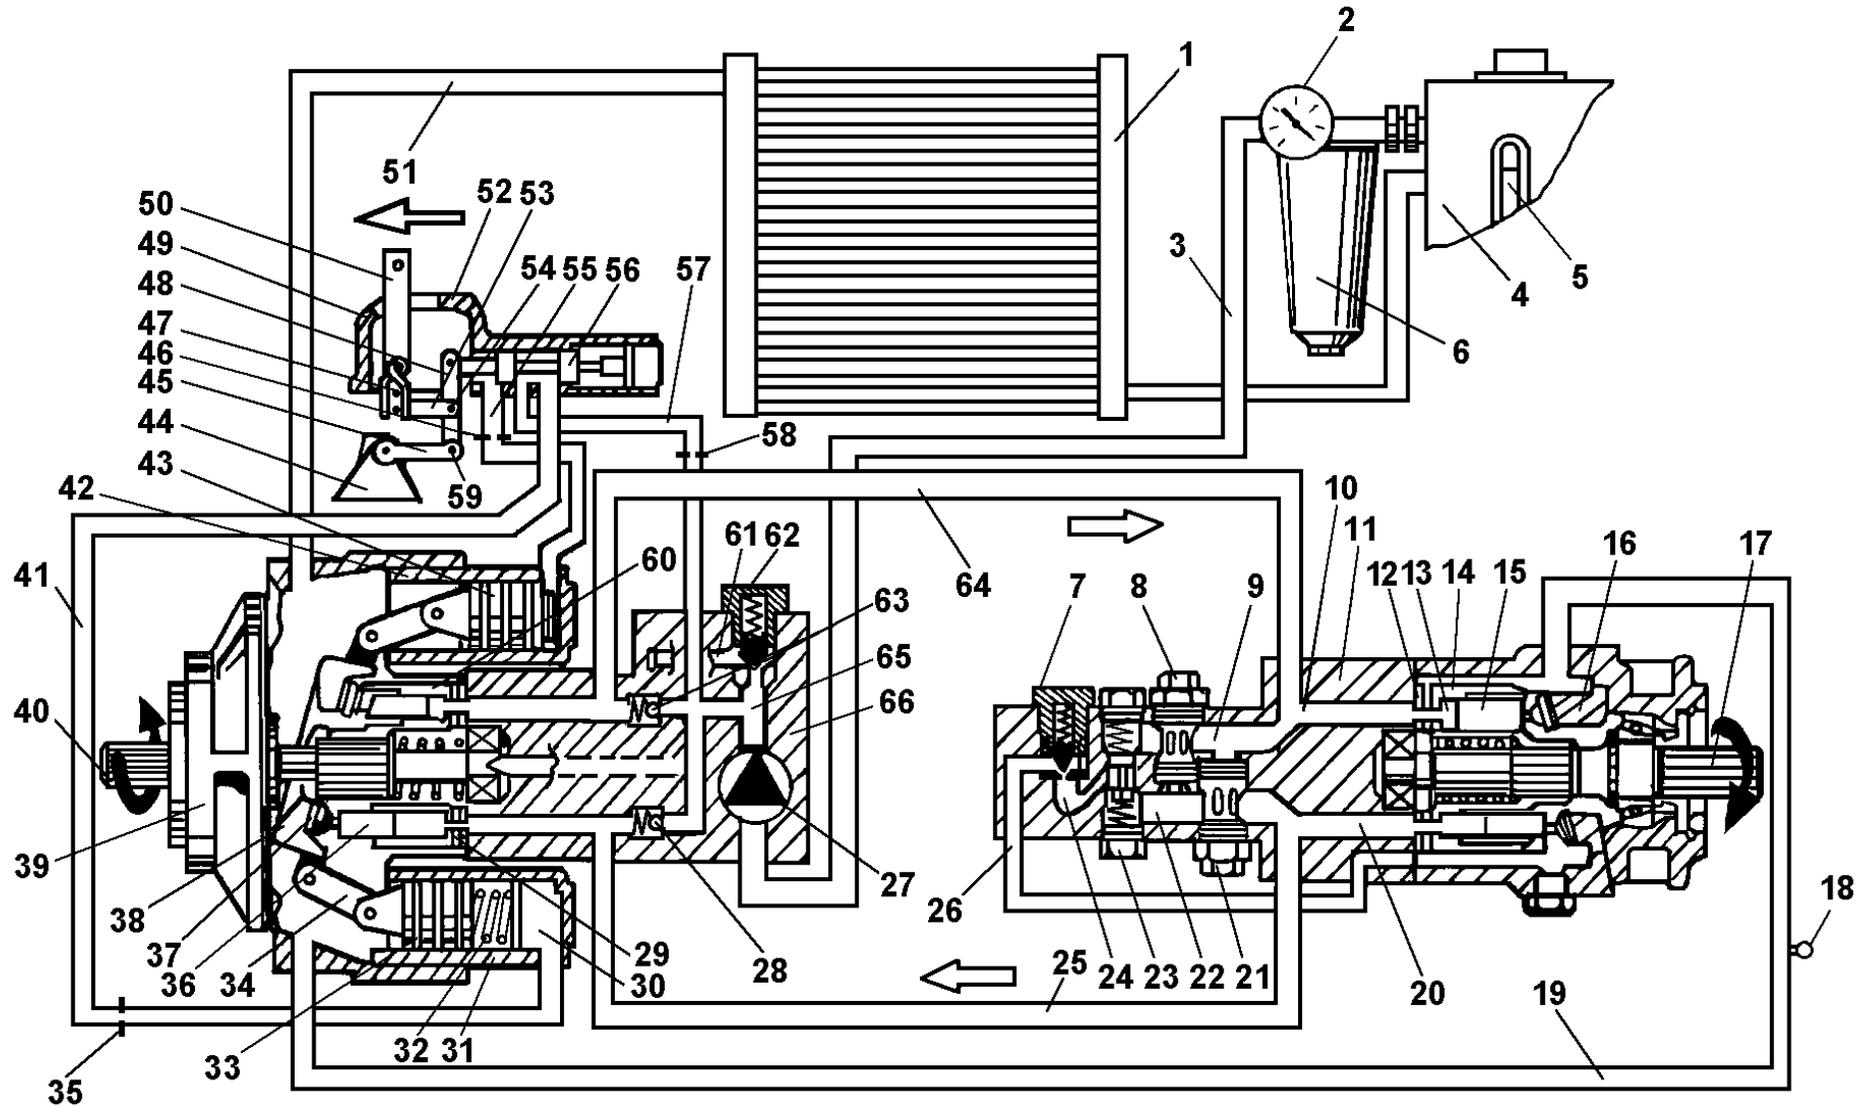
Конструктивная схема привода ГСТ-90 (движение вперед):
